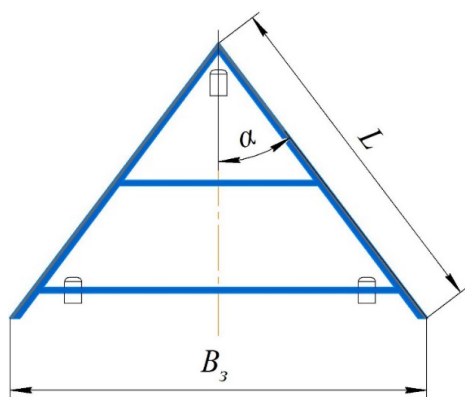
Схема разравнивателя-дернореза (вид сверху)
